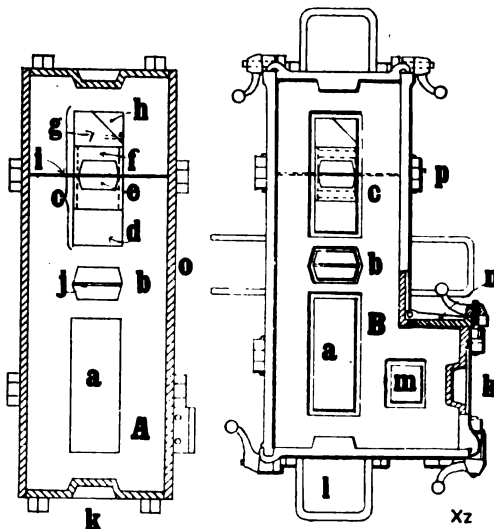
Ebener Schnitt durch zwei Palmer'sche Formmaschinen für gewöhnliche und Eckblöcke.
